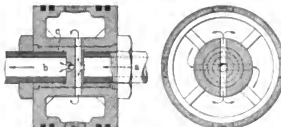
Z. A.: Wassergekühlter Kolben für Gasmotoren.
